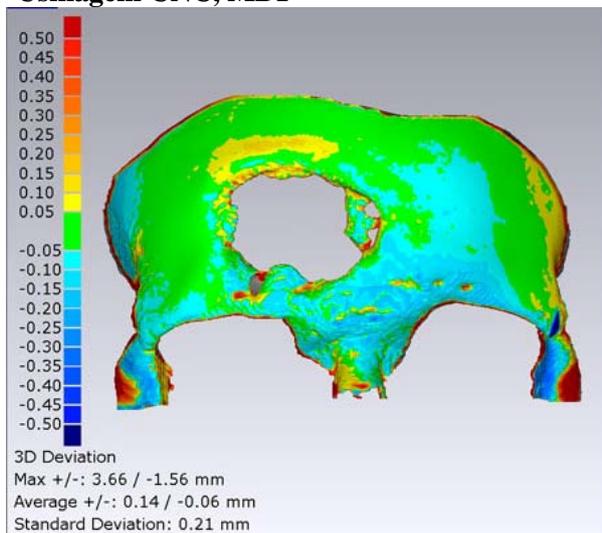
Precisão do protótipo fabricado por usinagem CNC de MDF.
